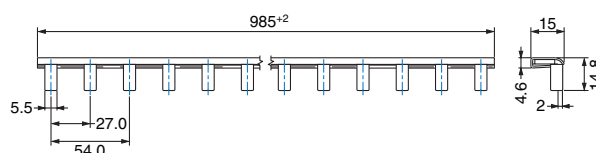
Dimensions de TMC 7...B1...CA (mm)
